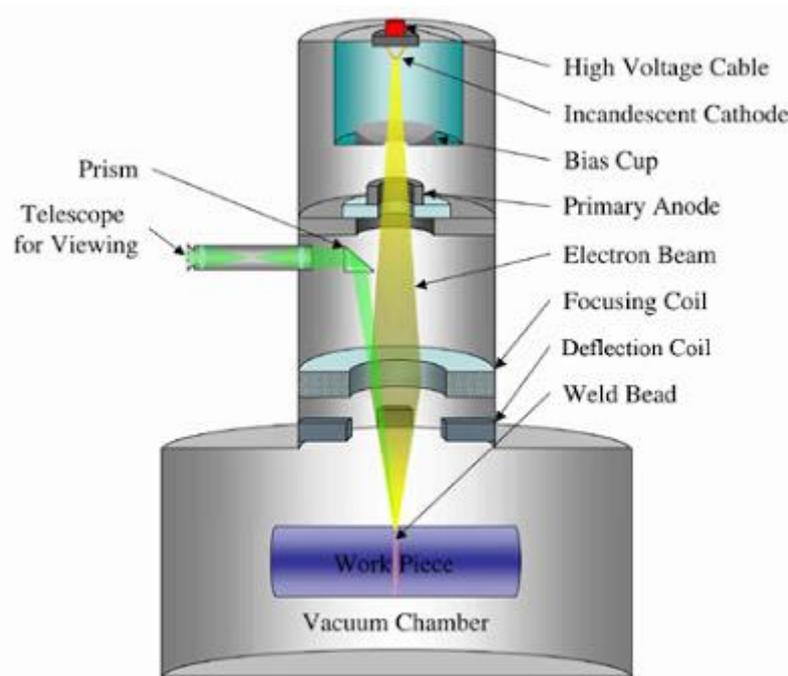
Esquema soldadura EBW (Fuente: mech4study.com)
